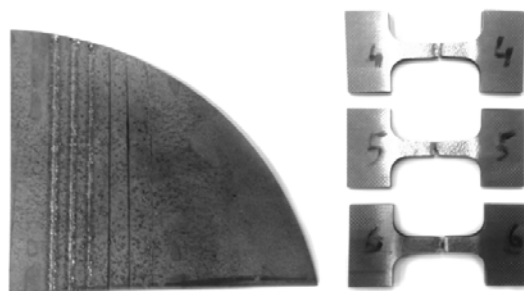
Внешний вид и лазерно-сваренные образцы сплава ЭИ689-ВД
